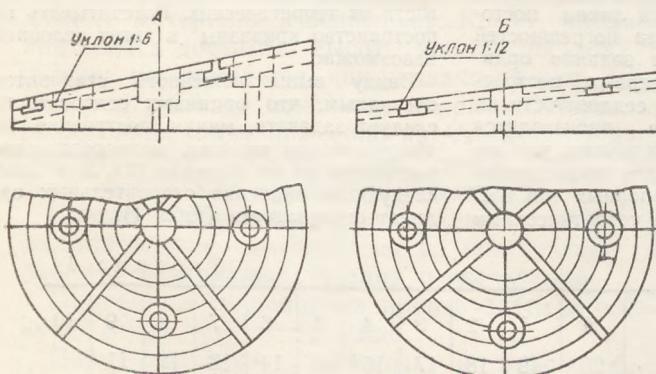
Кондукторы А и Б для проточки уплотняющих колец клина и гнезд корпуса клинкета
